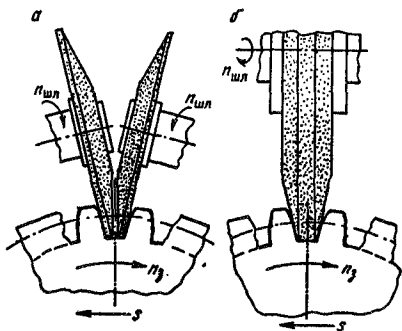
Схемы шлифования зубьев цилиндрических колес тарельчатыми (а) и дисковыми (б) кругами
